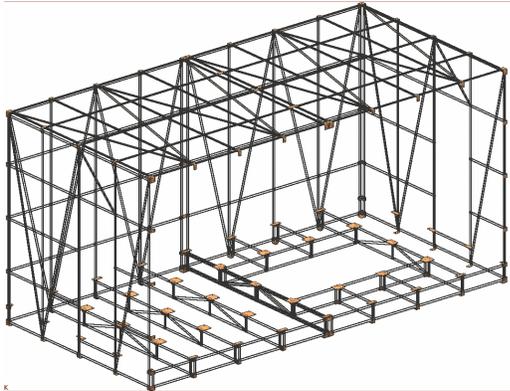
Außenwände, Fußboden und Decke einer Kabine mit Stützstrukturen in modularer Bauweise
